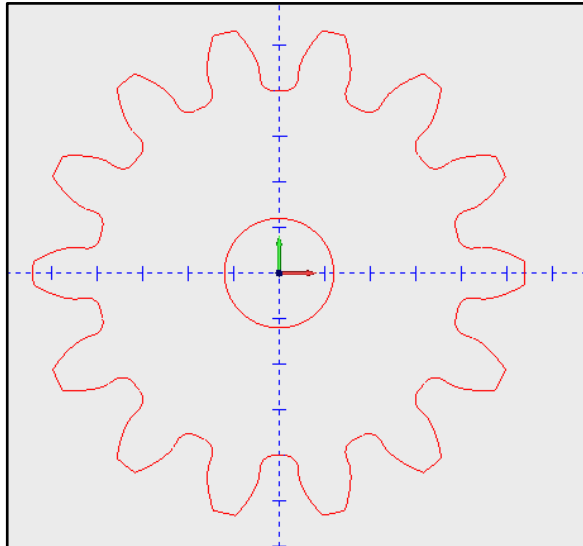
Diseño de la pieza B en el programa BobCAD – CAM
